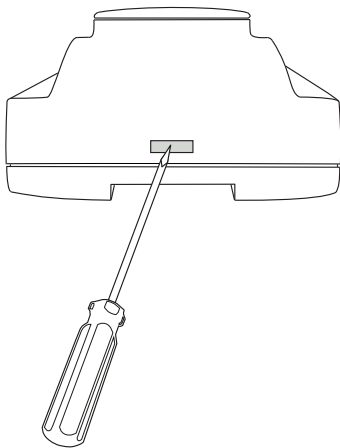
Entfernen der Oberseite des Gehäuses.
